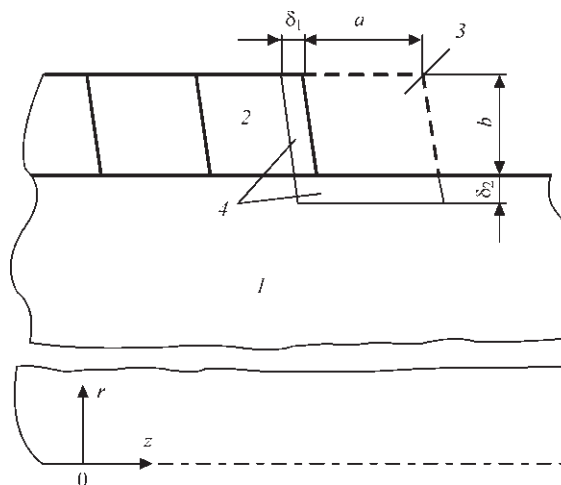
Схема заполнения (наплавки) N -го валика: 1 — деталь; 2 — ранее наплавленный $(N-1)$ -ый валик; 3 — область, отвечающая следующему N -ному валику и подлежащая заполнению (до заполнения — «пустая» область); 4 — нагреваемая сварочной дугой области приповерхностного объема в детали и ранее наплавленном валике; δ_1 — ширина нагреваемой области в материале валика $N-1$ при выполнении N -го валика; δ_2 — ширина нагреваемой области в основном металле при выполнении N -го валика; штрих-пунктирная линия — ось детали
